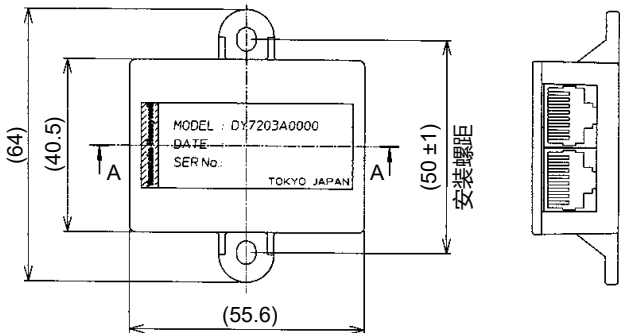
模块分支装置 (型号 DY7203A0000) (mm)
